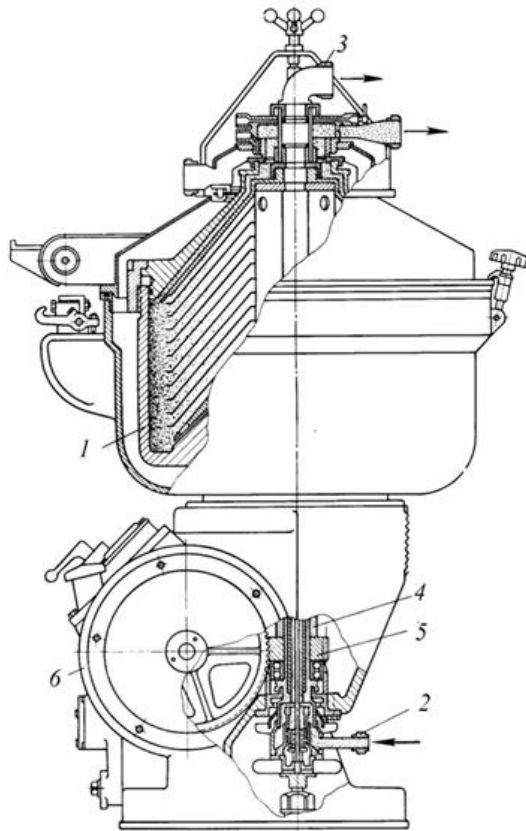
Загальний вид сепаратора: 1 – ротор; 2 – пристрій для подачі продукту; 3 – пристрій для виводу рідини; 4 – вертикальний вал; 5 - привідний механізм; 6 – станина
